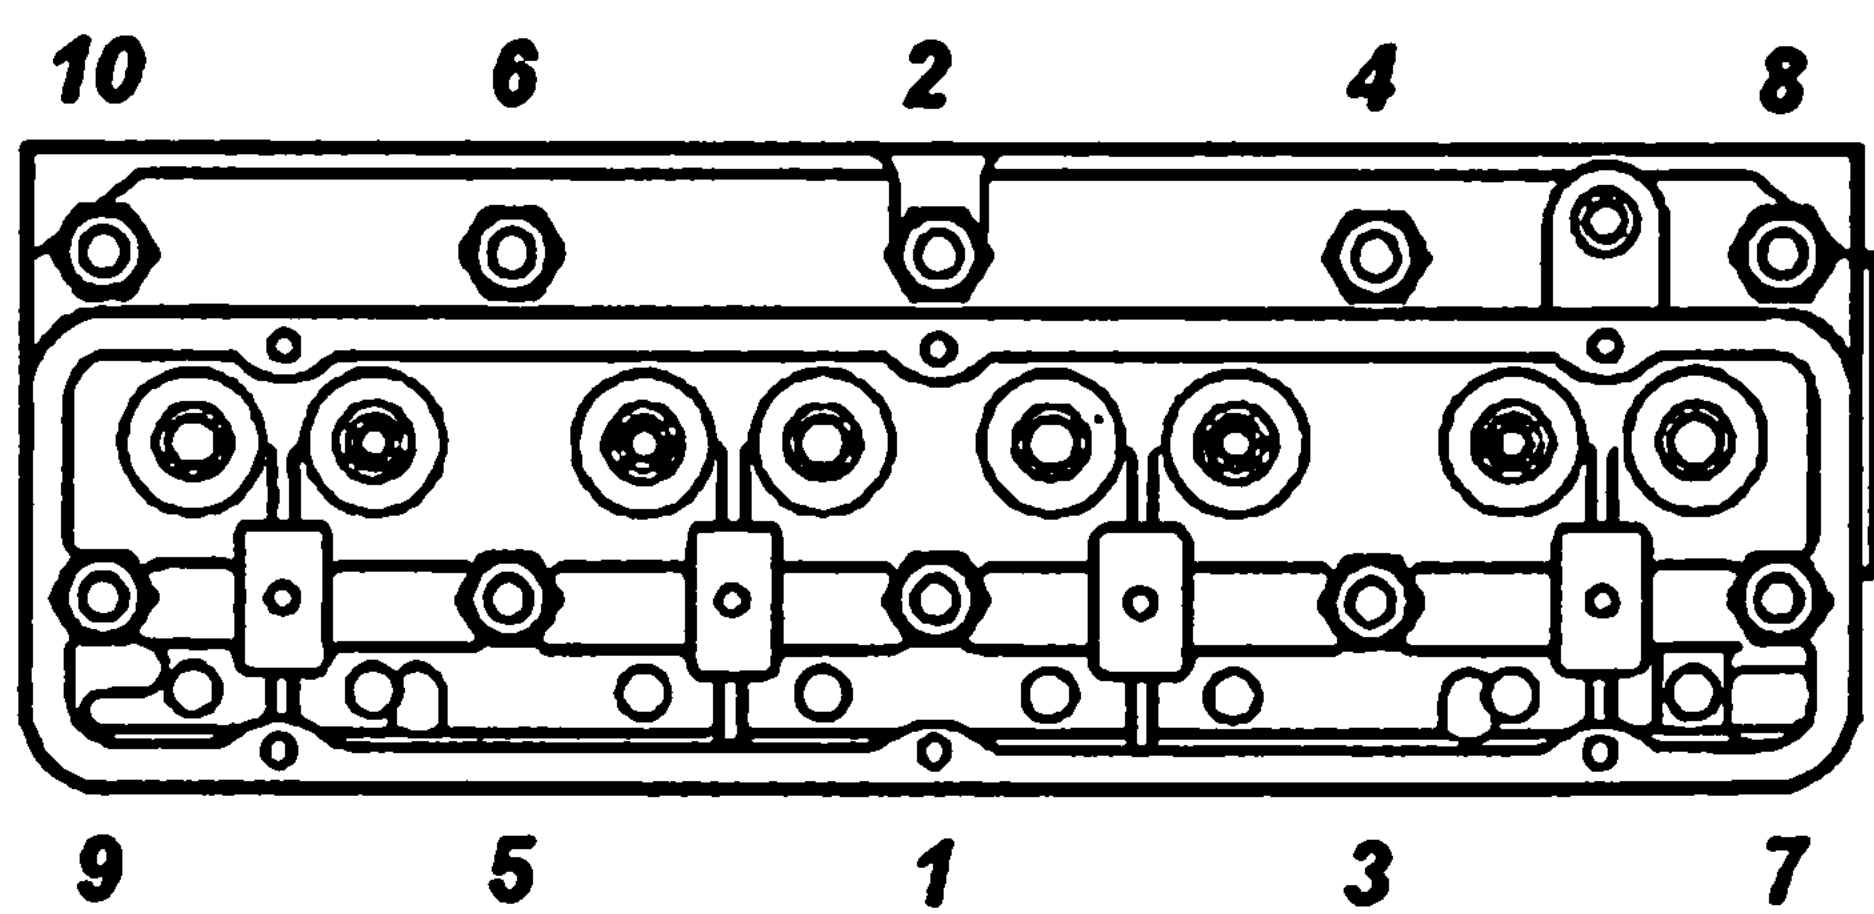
Порядок подтяжки гаек головки блока цилиндров
